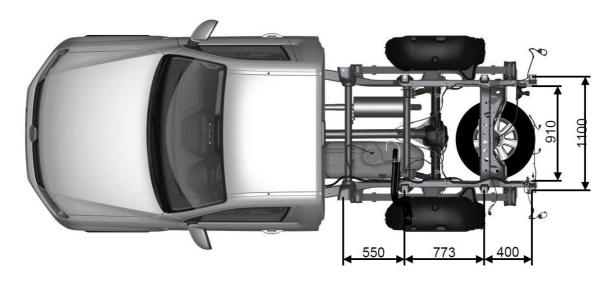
Vista dall'alto dell'Amarok SC (cabina singola) senza cassone
